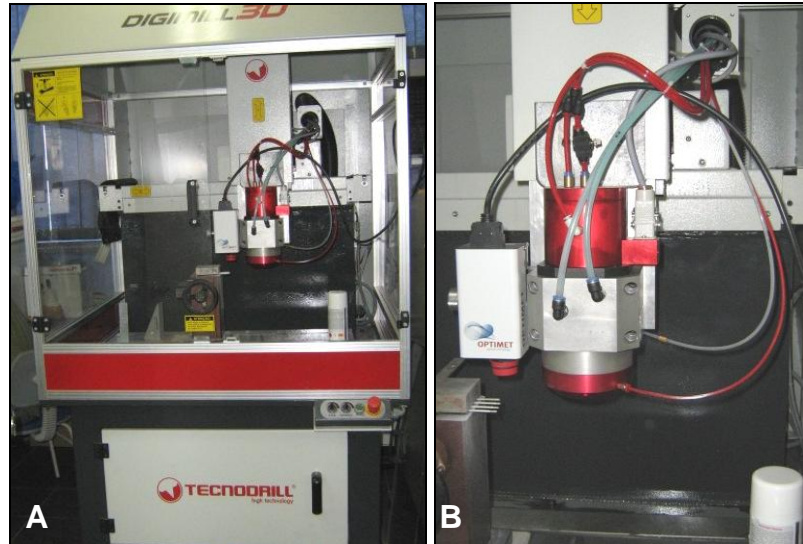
Em (A), equipamento de fresamento, scanner 3D e usinagem CNC Digimill®, e em (B), detalhe da parte onde é acoplada a ferramenta para usinagem. Equipamento pertencente ao LdSM, UFRGS
